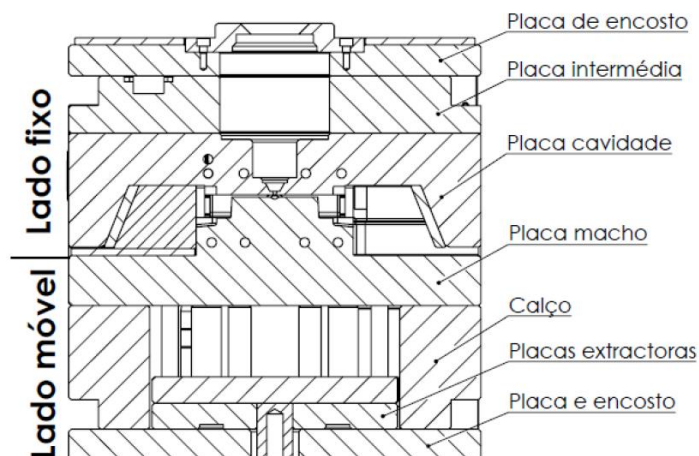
Esquema de um molde de injeção (Grupo Simoldes, 2017)
